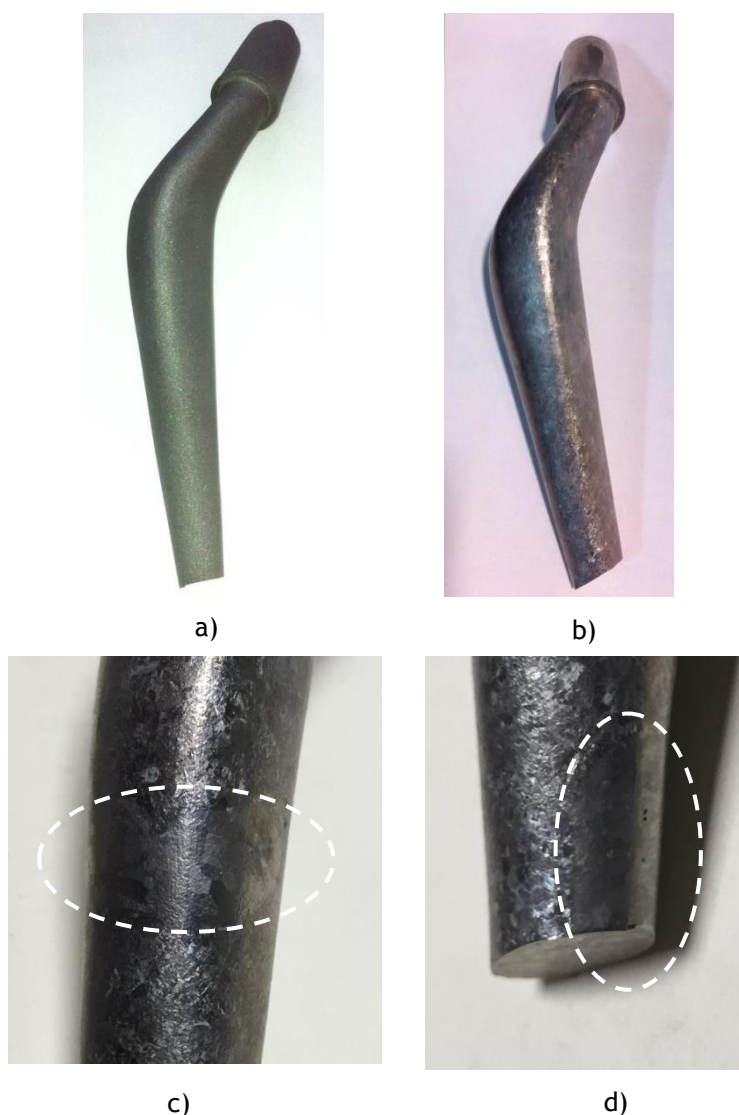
a) prótese após lixagem; b) prótese após maquinagem química; c) zona 1 reparada por soldadura; d) zona 3 reparada por soldadura
